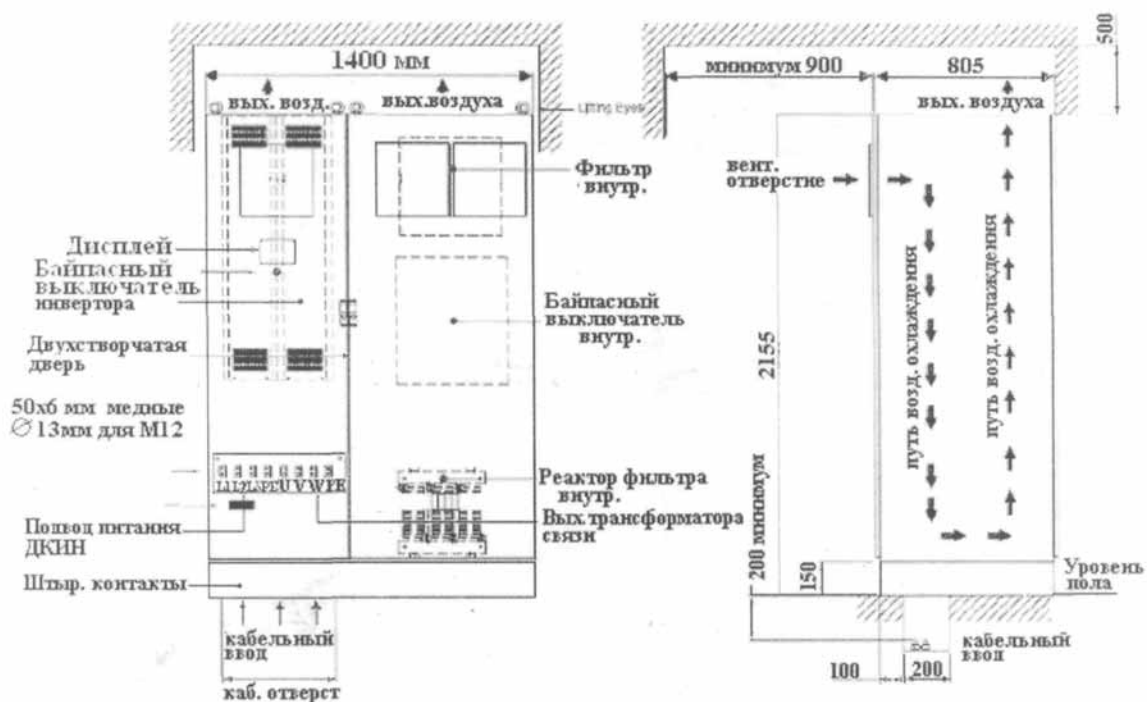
Габаритные размеры ДКИН на ток 700 А и напряжение 380 В
